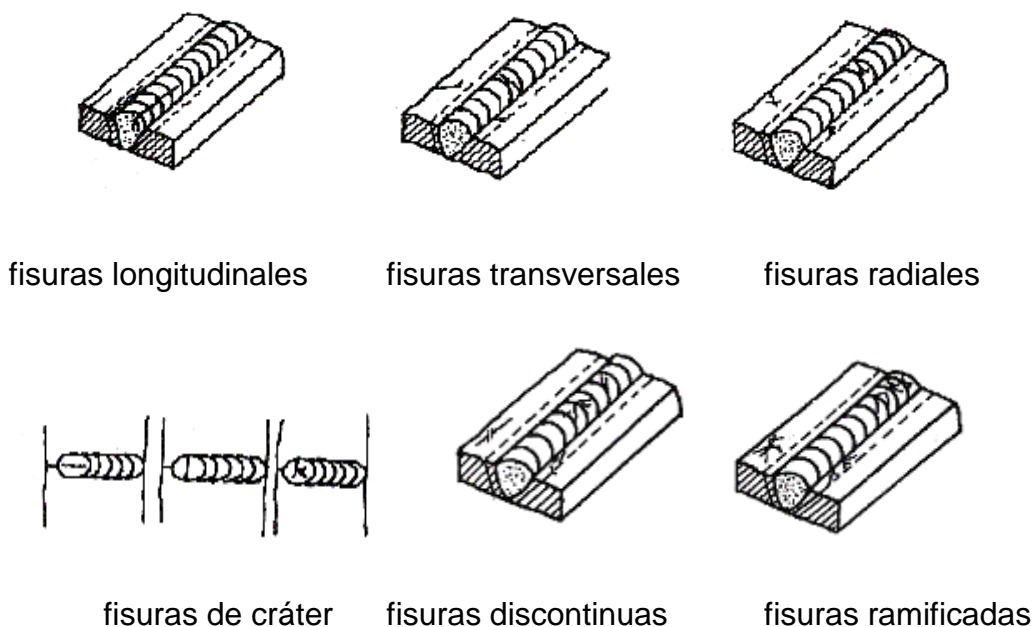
Clasificación de las fisuras
